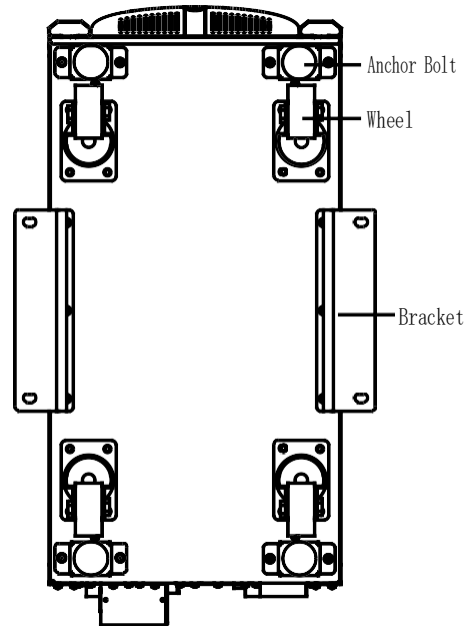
Soporte de Estructura (Vista por Debajo)
